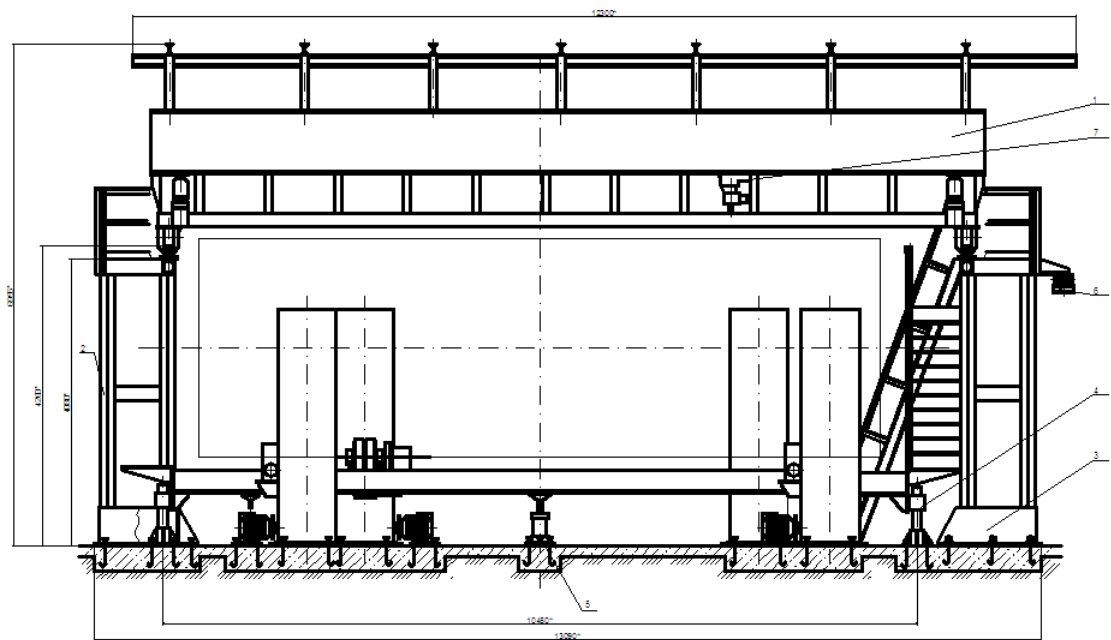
Стенд для зварювання повздовжнього розроблення кромки
